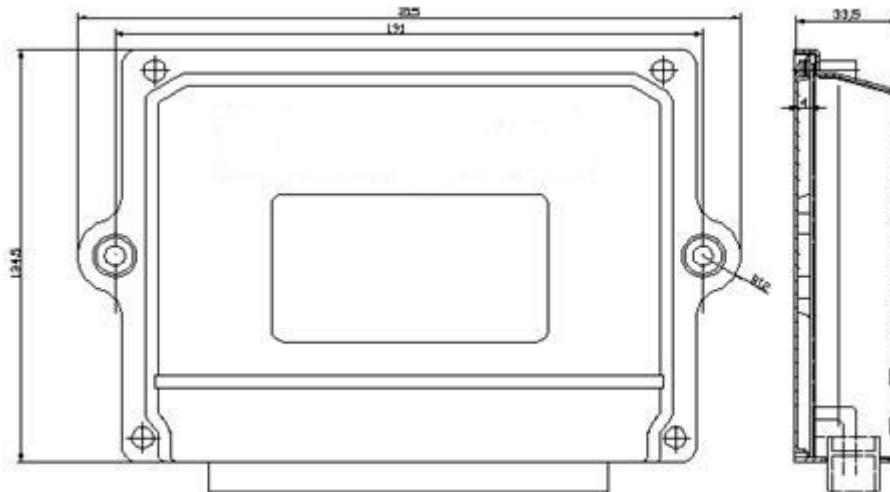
DK201,DK101 安装尺寸/Fig.6-2-1 Installing Dimension of DK201 and DK101
